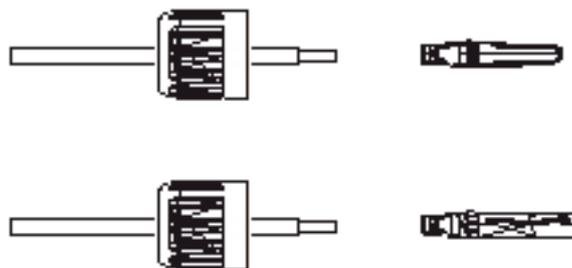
Inserte el cable en el conector Tuerca ciega y pin de contacto
